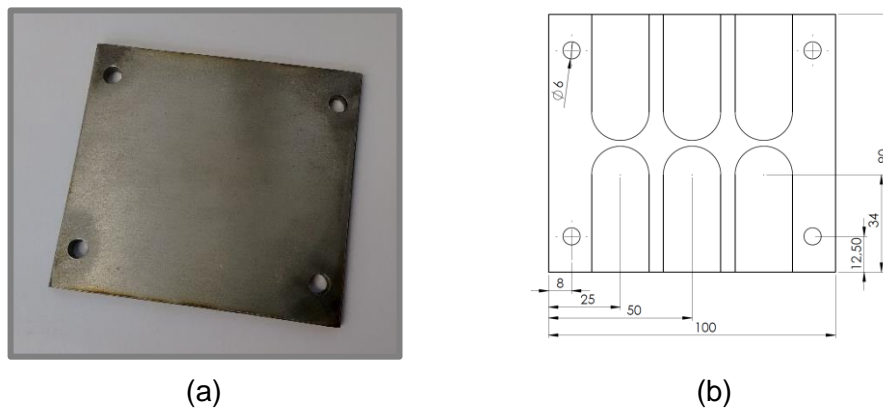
Corpo de prova (CP): (a) imagem do CP preparado para usinagem; (b) croqui do CP pós-usinagem.
